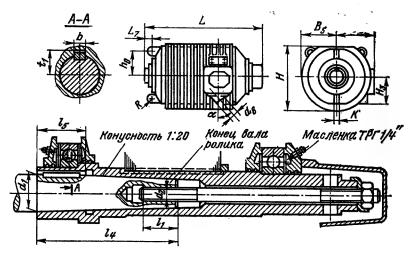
Габаритные и установочиые размеры двигателей серии APK 4—7-го габаритов.
